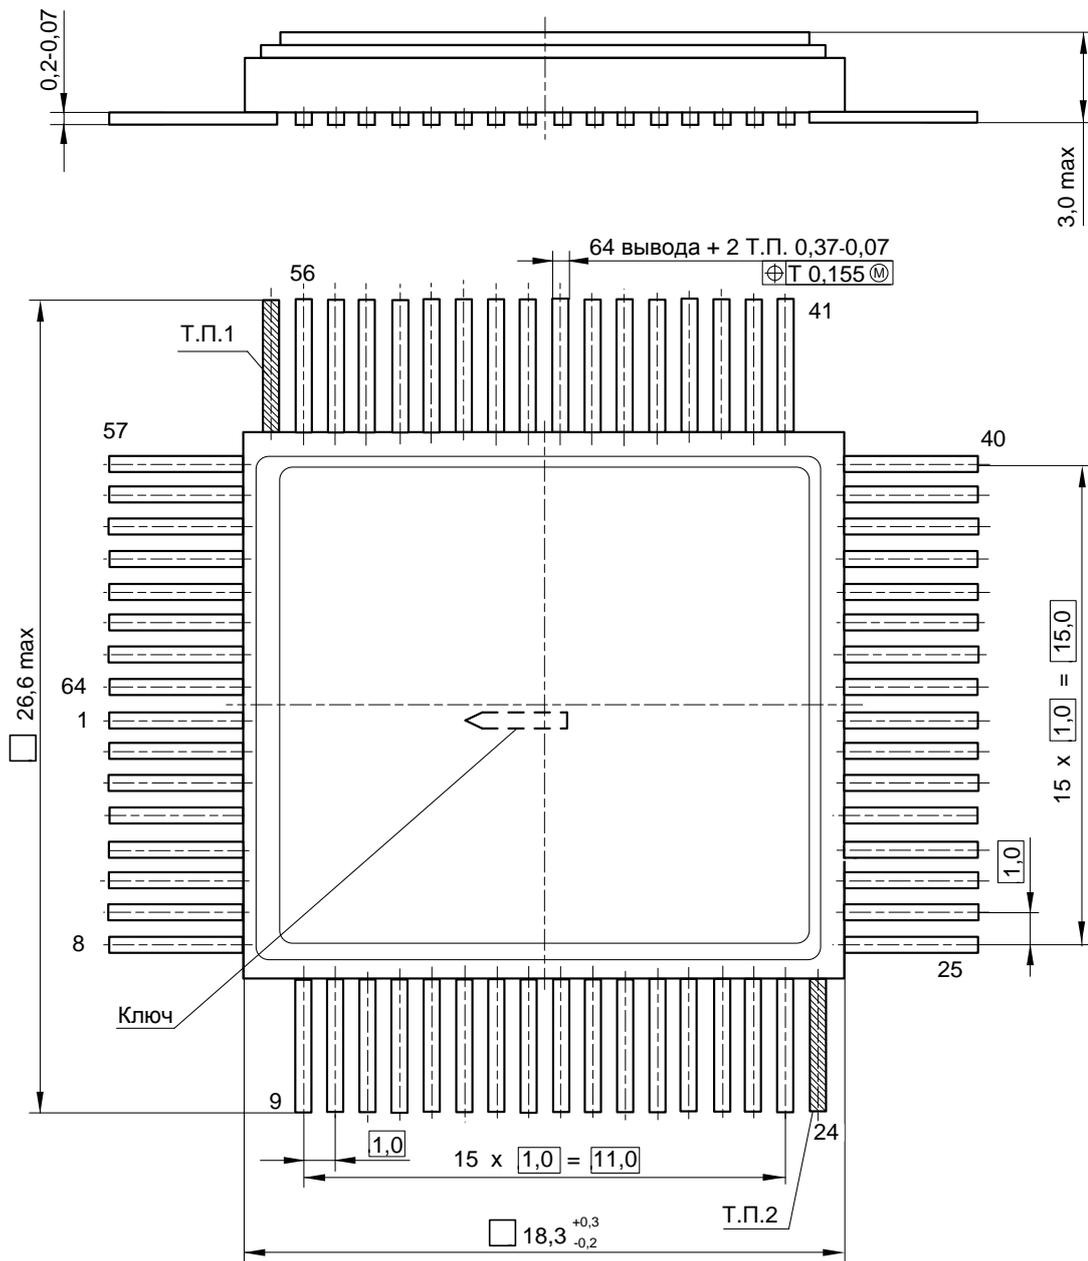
Габаритный чертеж микросхемы в корпусе Н18.64-3В
